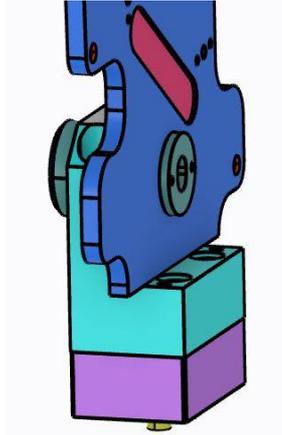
Detalle inferior del útil de posicionado de barras en costillas de celosía
